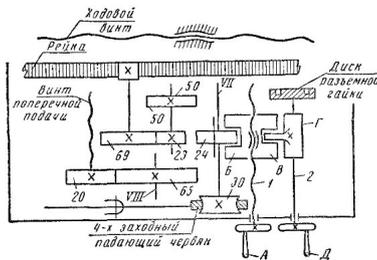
Блокировочный механизм токарно-винторезного станка 1А62
